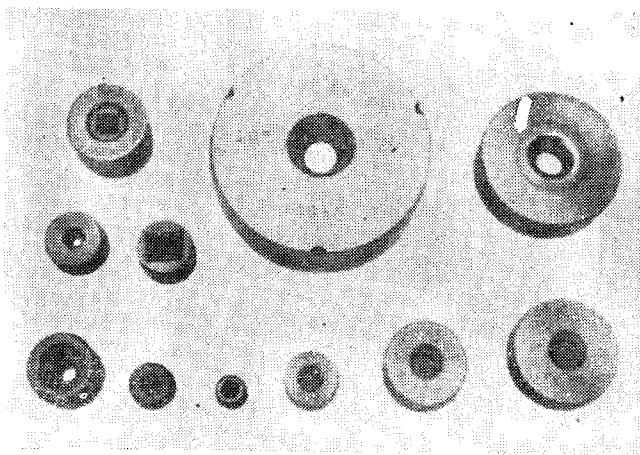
Внешний вид заготовок, готовых волок и волоочильных плашек
